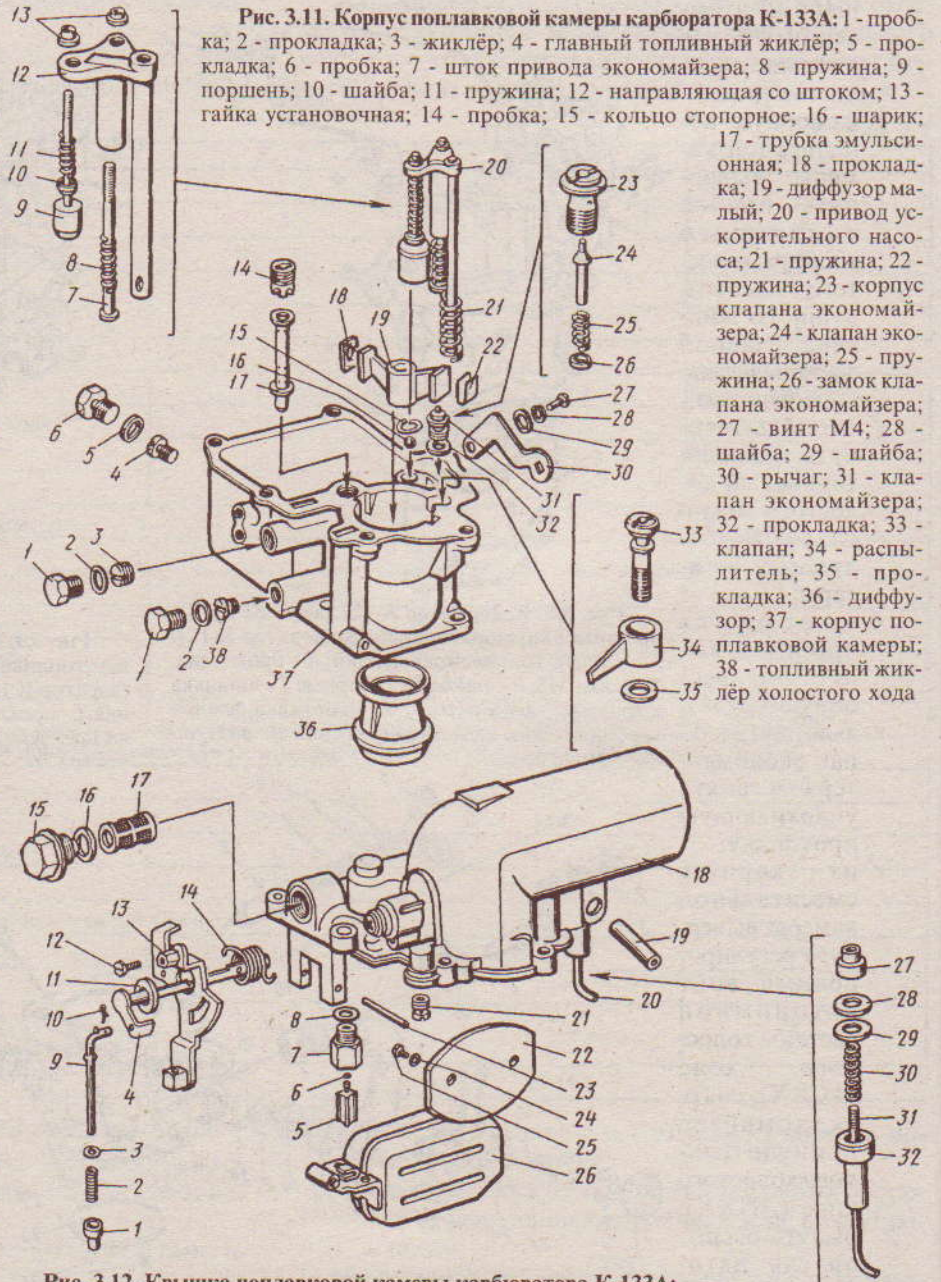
Корпус поплавковой камеры карбюратора К-133А: 1 - пробка; 2 - прокладка; 3 - жиклёр; 4 - главный топливный жиклёр; 5 - прокладка; 6 - пробка; 7 - шток привода экономайзера; 8 - пружина; 9 - поршень; 10 - шайба; 11 - пружина; 12 - направляющая со штоком; 13 - гайка установочная; 14 - пробка; 15 - кольцо стопорное; 16 - шарик;
